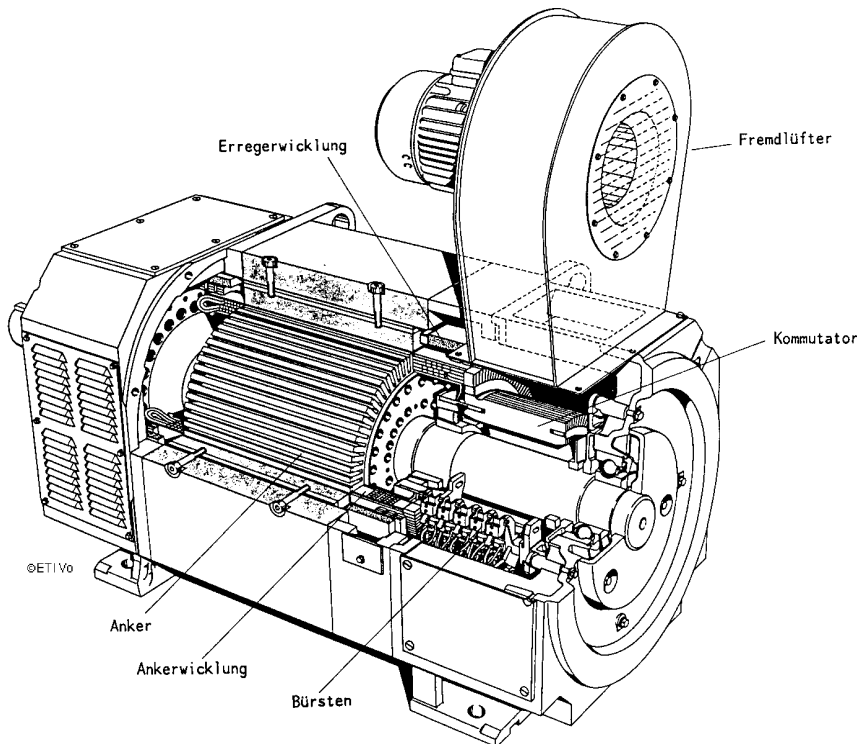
Teilschnittbild einer Gleichstrommaschine mit aufgesetztem Lüfter
